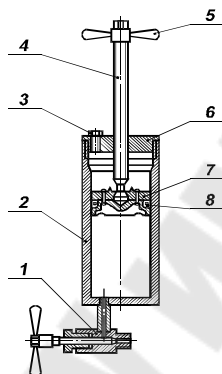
Пресс-бачок:1 – запорный механизм; 2 – корпус; 3 – пробка; 4 – винт; 5 – вороток; 6 – крышка; 7 – поршень; 8 – кольцо
